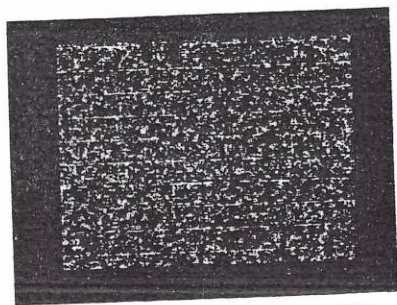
Padrão de speckle de uma amostra de aço AISI1020 usinado com fresa frontal.
